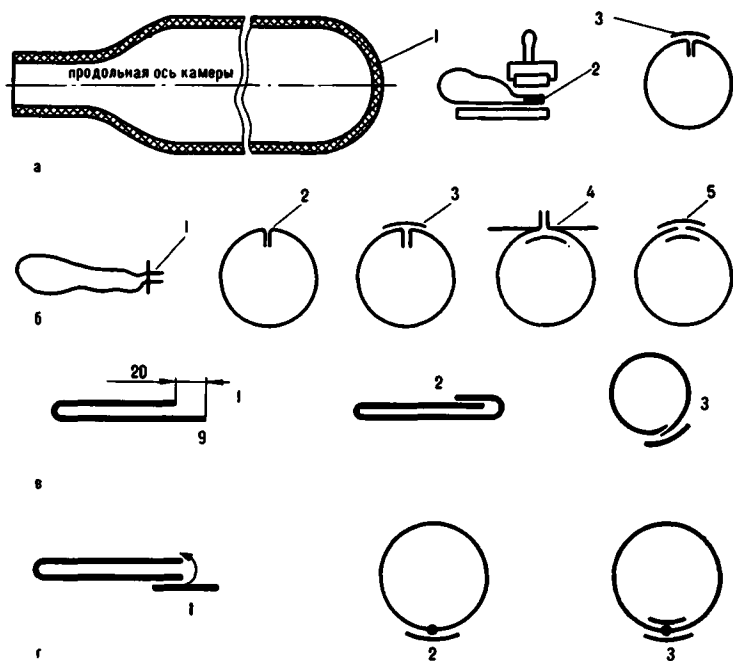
Способы изготовления камер и цельноклеевых поплавков:
